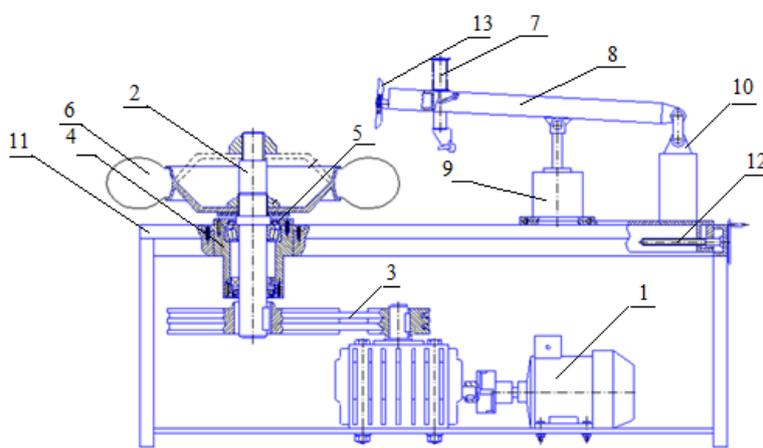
Стенд для демонтажа шин: 1 – привод; 2 – рабочий вал; 3 – гибкая передача; 4 – коробка для подшипников; 5 – текстолитовая пластина; 6 – колесо; 7 – ролик; 8 – демонтажный рычаг; 9 – пневмоцилиндр; 10 – кронштейн; 11 – рама; 12 – ходовой винт; 13 – лапка
